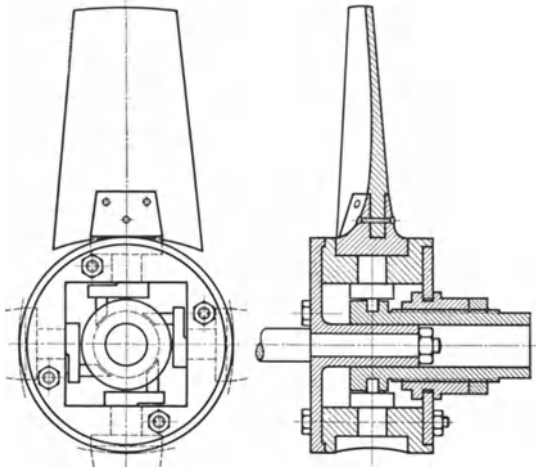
Verstellmechanismus für vierblättrige Holzschrauben.
